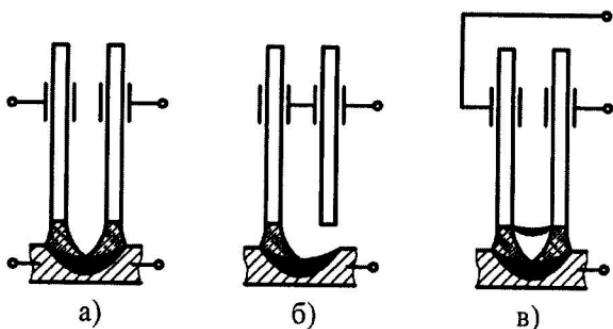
Схеми багатодугового зварювання: а – двома дугами, б – розщепленим електродом; в – трифазною дугою
